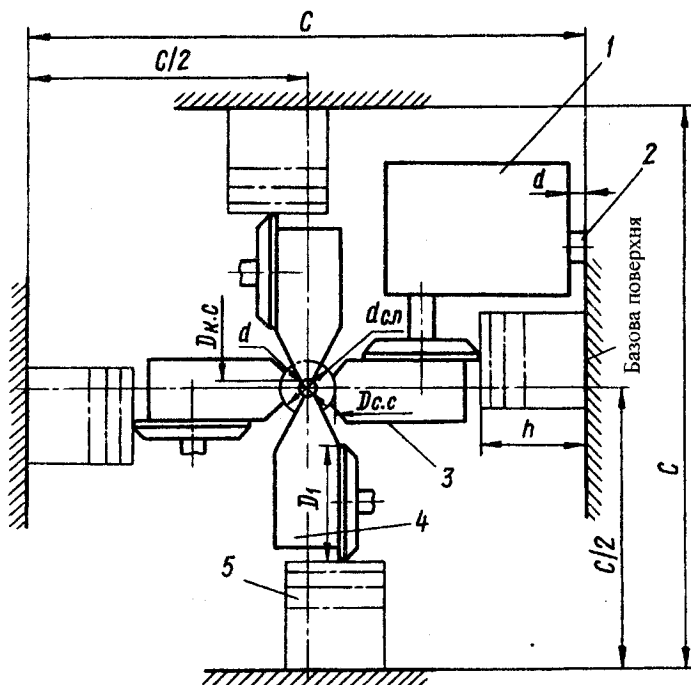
Схема поздовжньо-гвинтового прокатування свердел
